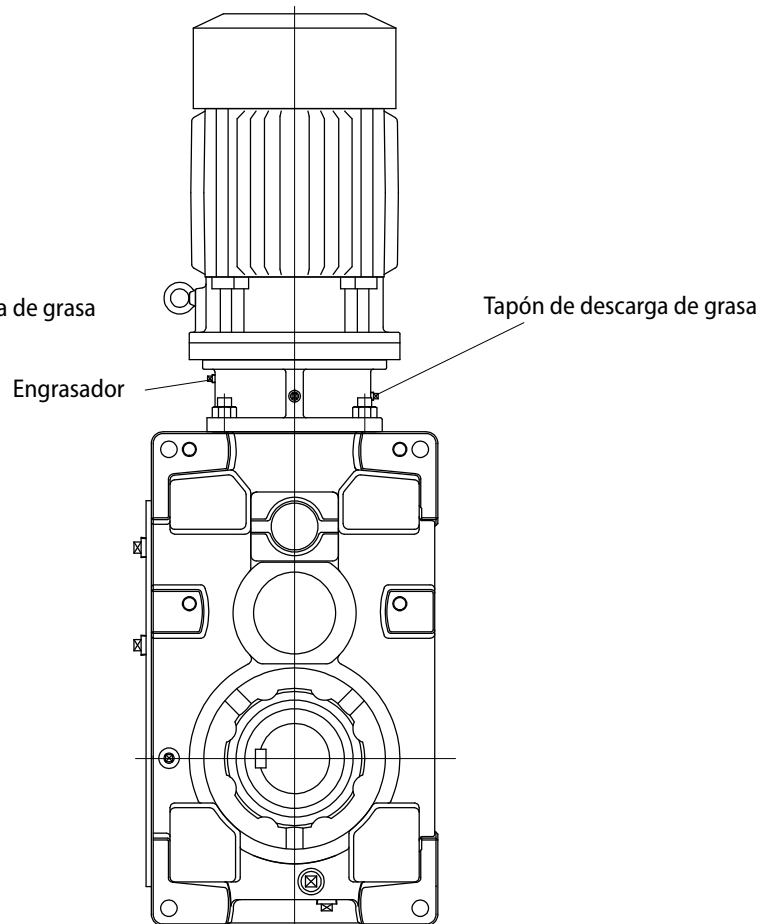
Unidad de accionamiento, montaje perpendicular
